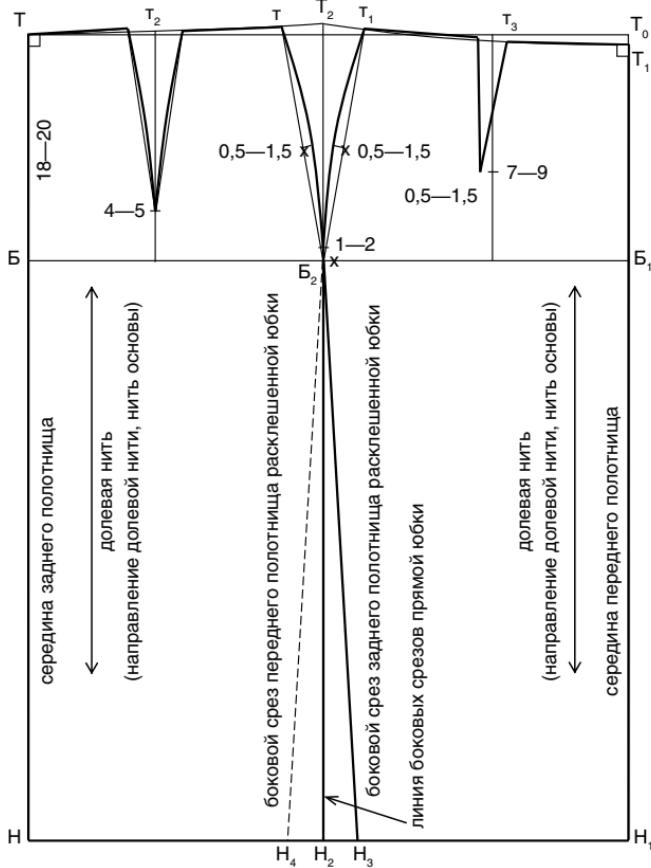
Чертеж базовой конструкции юбки (двухшовная юбка с шестью вытачками по линии талии)
